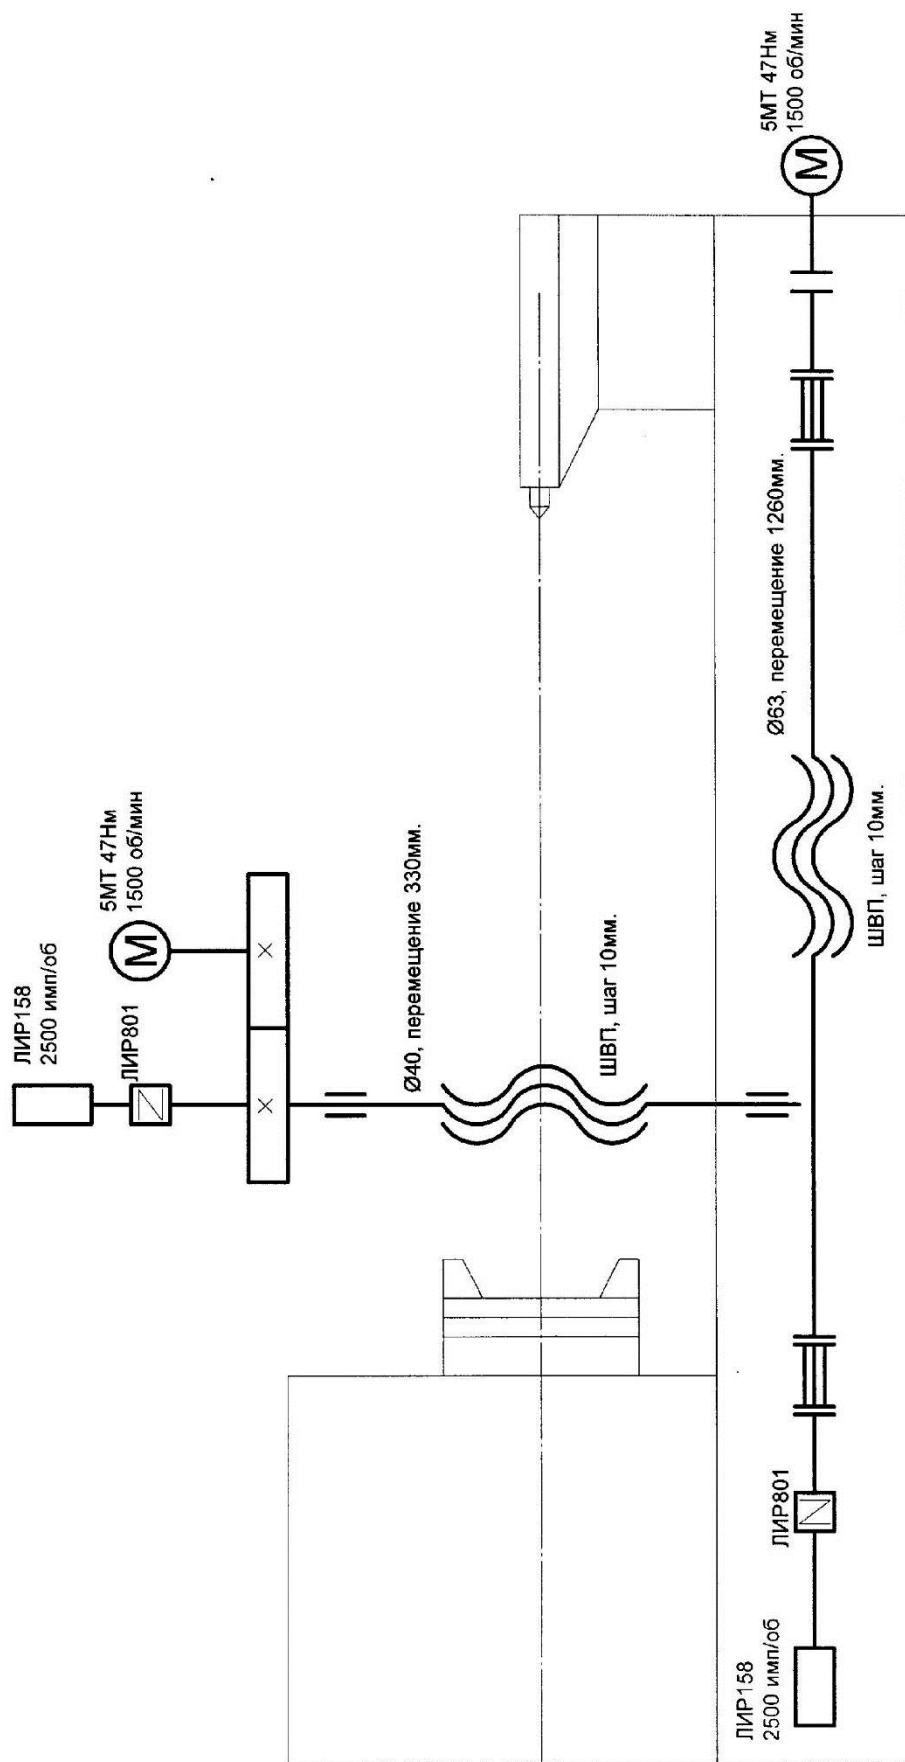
Кинематическая схема токарного станка модели 16К30 Ф323
